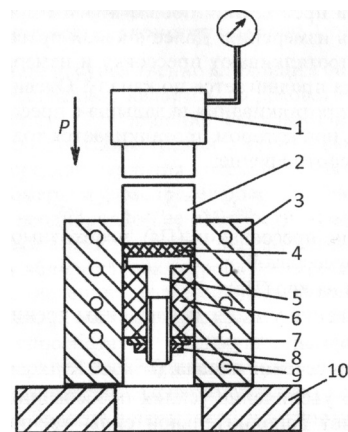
Устройство для определения оптимальной величины давления прессования: 1 – источник давления, 2 – пуансон, 3 – матрица, 4 – спрессованный образец, 5 – верхний диск вкладыша с резьбовым наконечником, 6 – средний деформируемый диск вкладыша, 7 – нижний диск вкладыша, 8 – регулировочная гайка вкладыша, 9 – нагреватели, 10 – подставка
